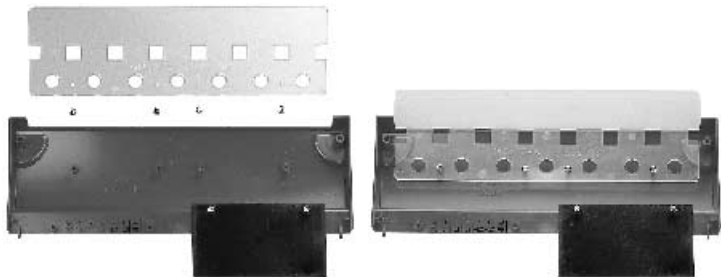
Защитный кожух для MOVITRAC® 07 типоразмера 4 01470BXX
